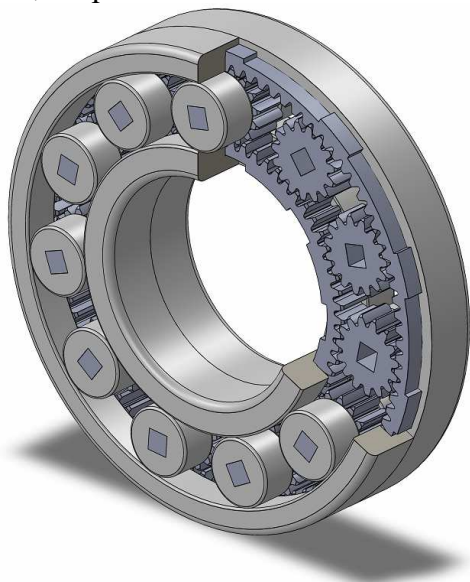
Бессепараторный подшипник с зубчатым зацеплением в разрезе
